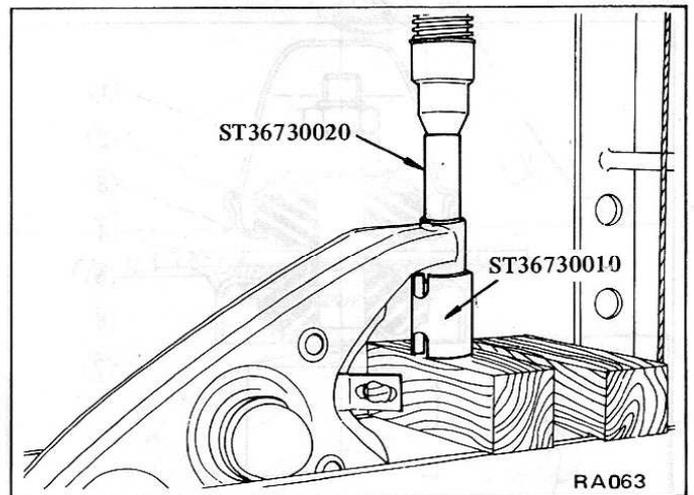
Dépose d'une bague du bras de suspension arrière
